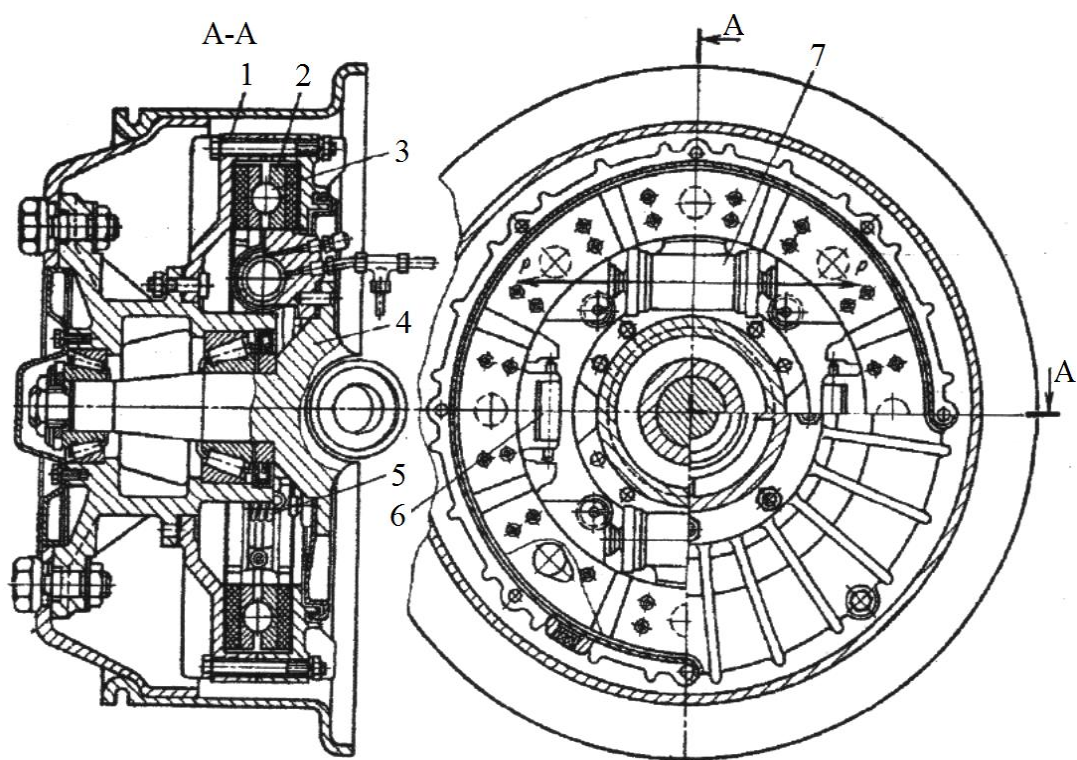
Дисково-колодкове гальмо НАМІ-ЛАЗ: 1 - корпус; 2 - натискний диск; 3 - кулька; 4 – нерухома напіввісь колеса; 5 - пружина; 6 - автоматичний компенсатор зносу фрикційних накладок; 7 - гідроциліндр
